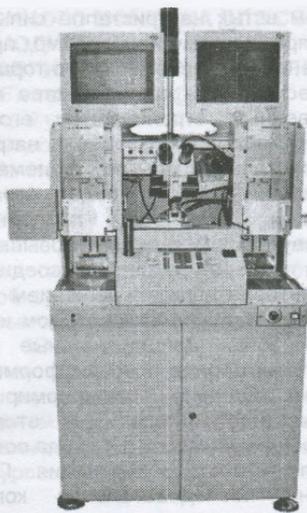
Установка ультразвуковой сварки ЭМ-4020ПМ
